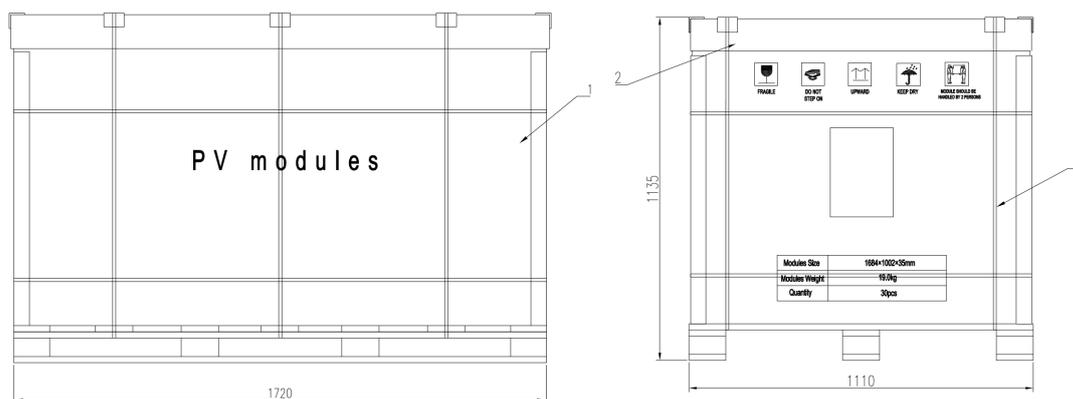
Lado largo del embalaje (izquierda) y lado corto (derecha) (dimensiones en mm)
